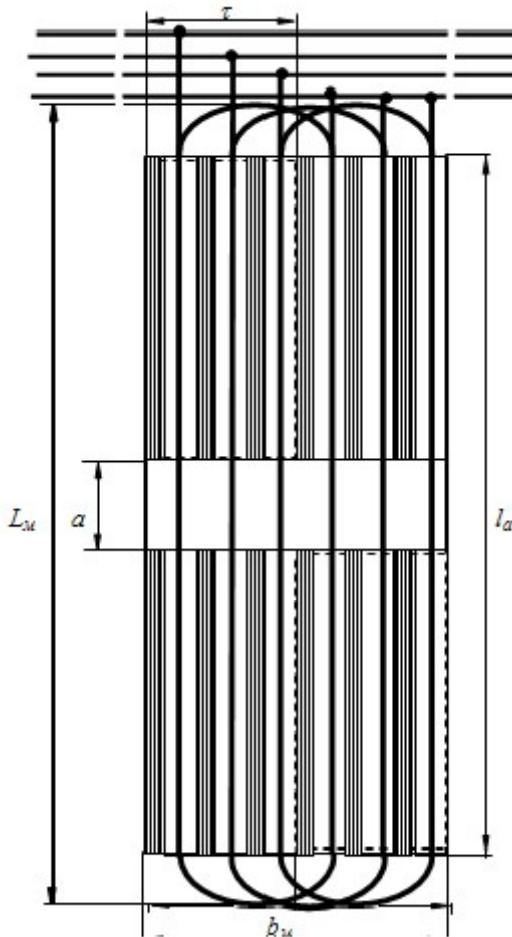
Індуктор блока-модуля ЛТЕД з трифазною обмоткою(вид зверху)
